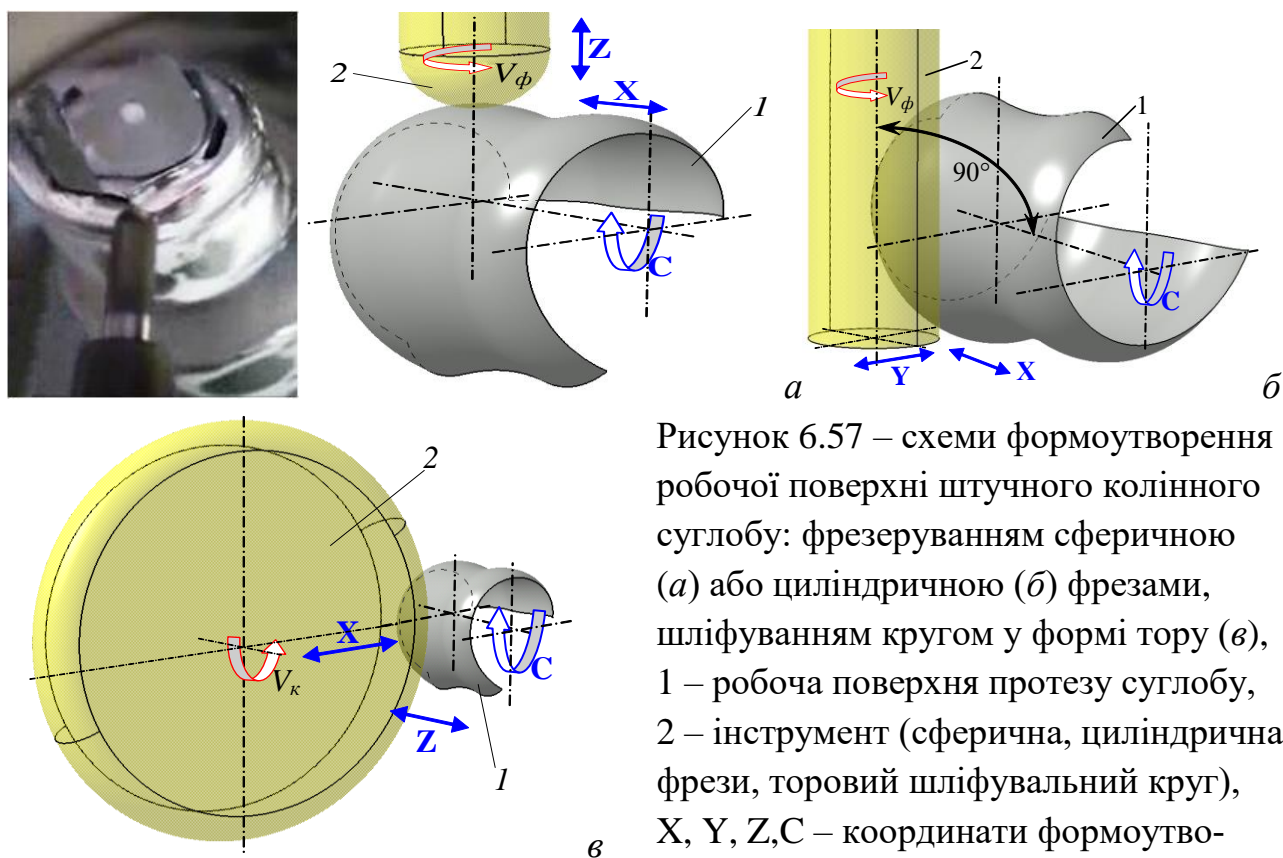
схеми формоутворення робочої поверхні штучного колінного суглобу: фрезеруванням сферичною (а) або циліндричною (б) фрезами, шліфуванням кругом у формі тору (в), 1 – робоча поверхня протезу суглобу, 2 – інструмент (сферична, циліндрична фрези, торовий шліфувальний круг), X, Y, Z, C – координати формоутворення верстату з ЧПК, V_ϕ – швидкість обертання інструменту.
